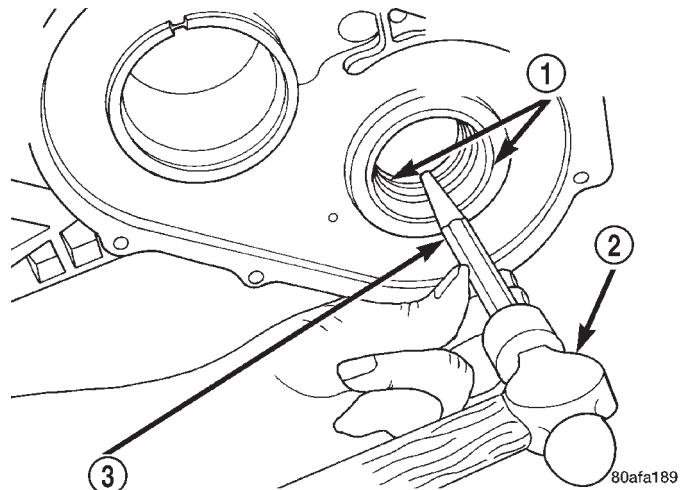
Desmontaje de la cubeta interna del cojinete transmisor
